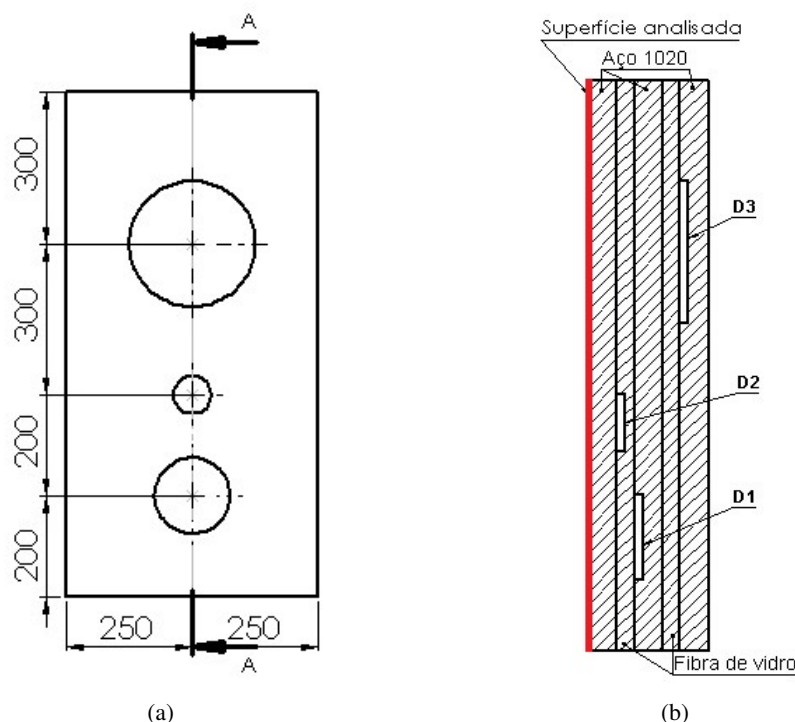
Desenho da amostra (mm) (a) vista superior e (b) corte A-A
